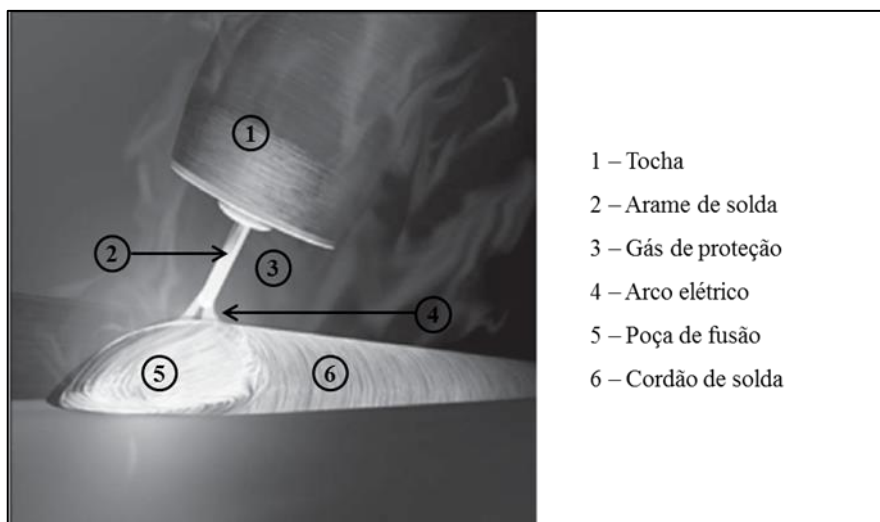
Processo de soldagem GMAW (ERICA, 2015).
